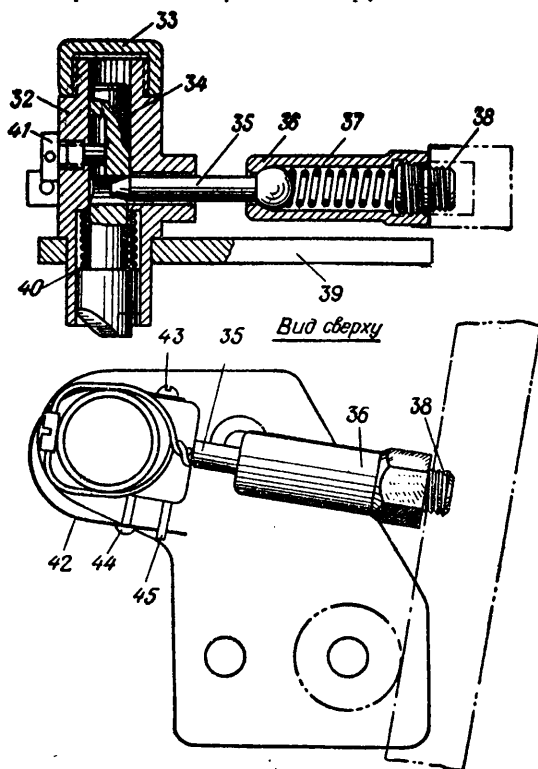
Задержник (С601-6) старой конструкции: 32 — корпус (С601-5); 33 — колпак; 34 — стержень задержника (01-20); 35 — палец (01-24); 36 — соединительная втулка (01-23); 37 — пружина пальца (01-25); 38 — соединительный винт (01-26); 39 — планка (01-19); 40 — пружина задержника (01-21); 41 — винт для удержания задержника (01-35); 42 — пластинчатая пружина (02-64); 43 — винт (01-67); 44 — стопор (01-66); 45 — скоба
